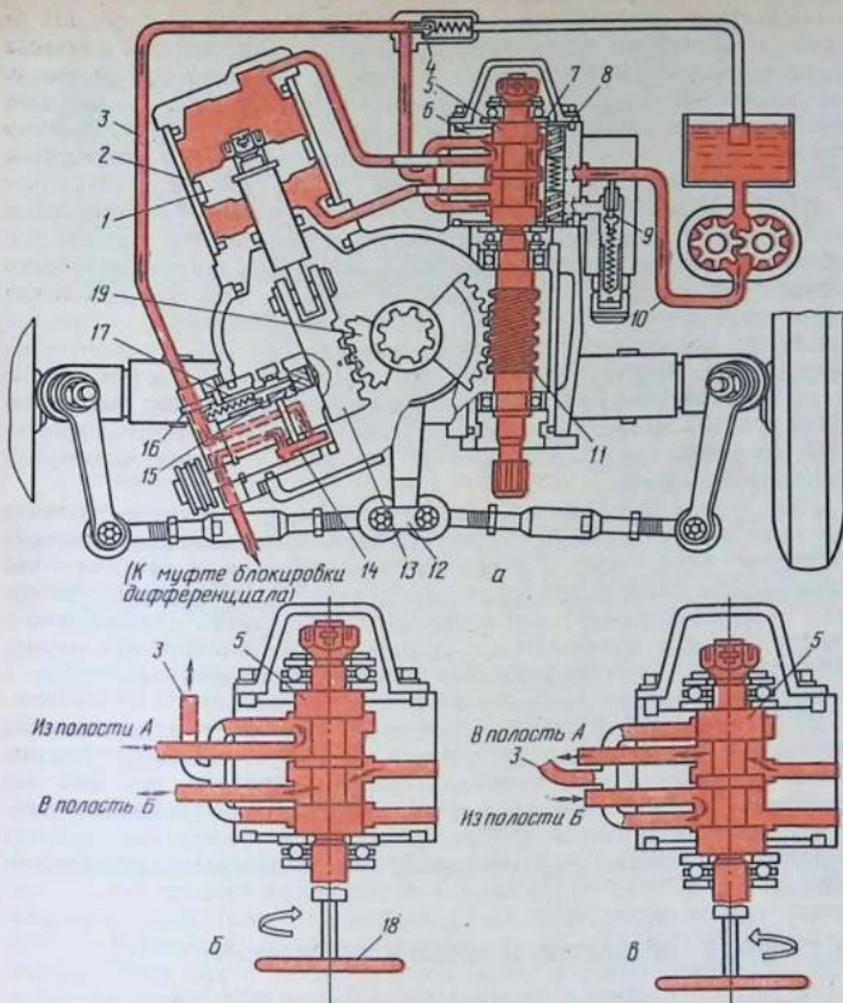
Схема гидроусилителя трактора МТЗ-80:
